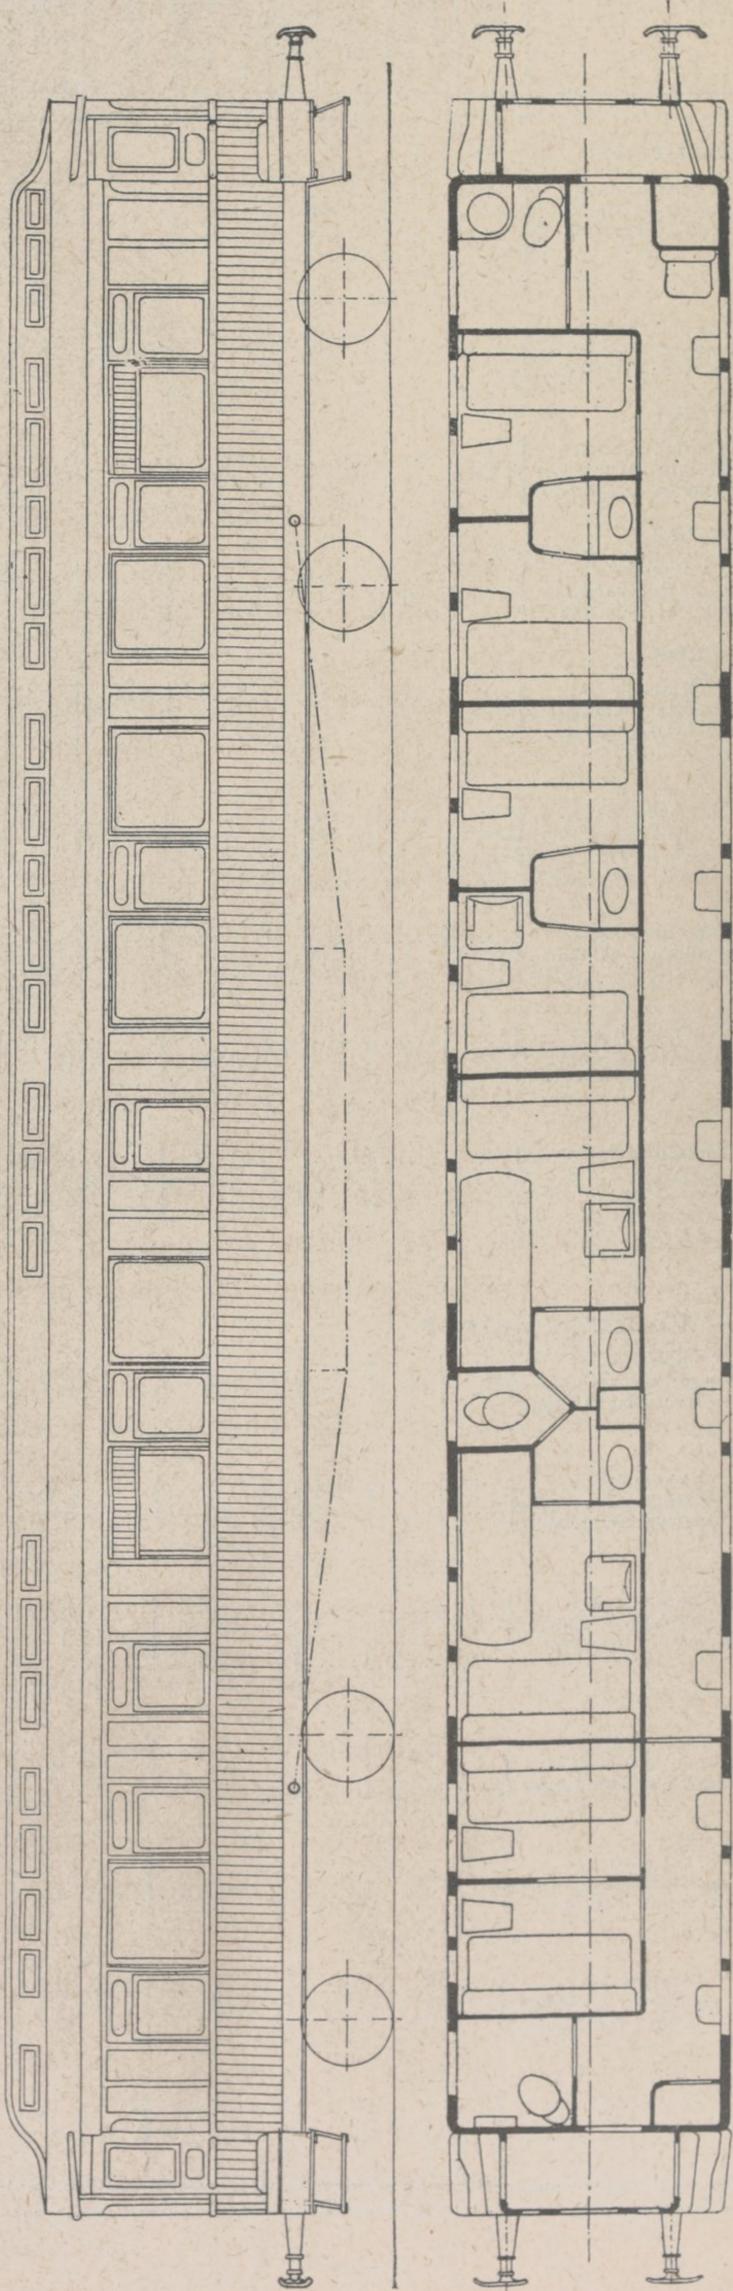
VOITURE CONSTRUITE EN 1909.
